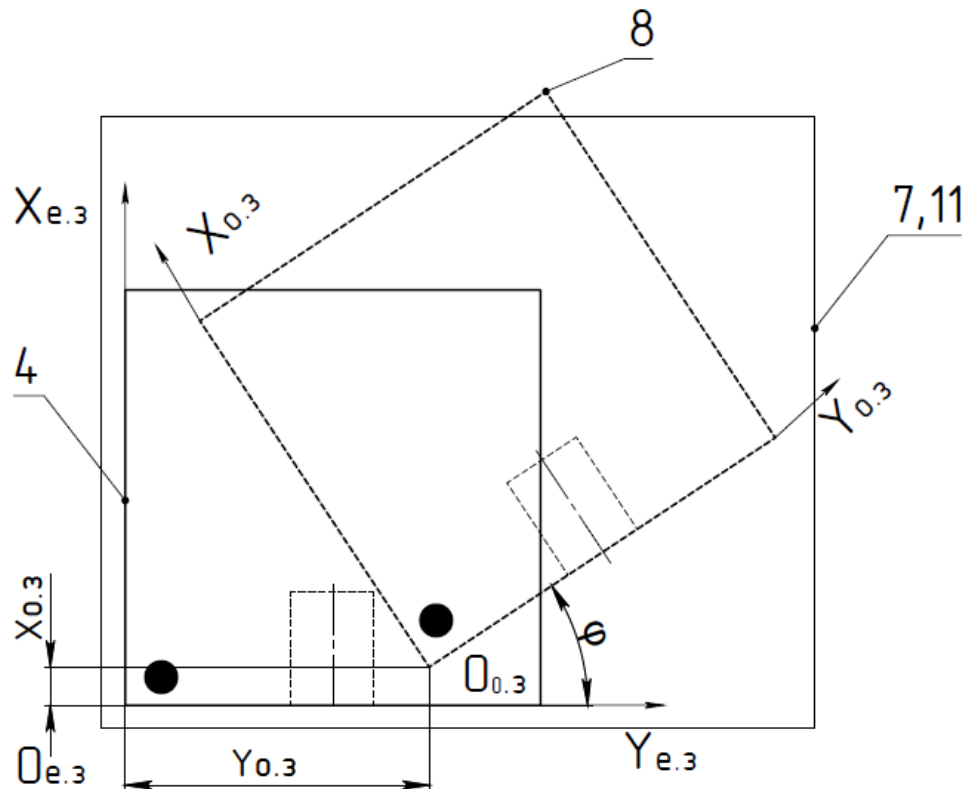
Зображення оброблюваної заготовки, на яке накладено зображення еталонної заготовки
